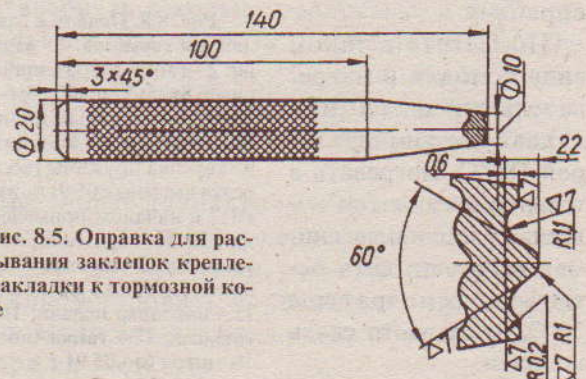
Оправка для расклепывания заклепок крепления накладок к тормозной колодке
